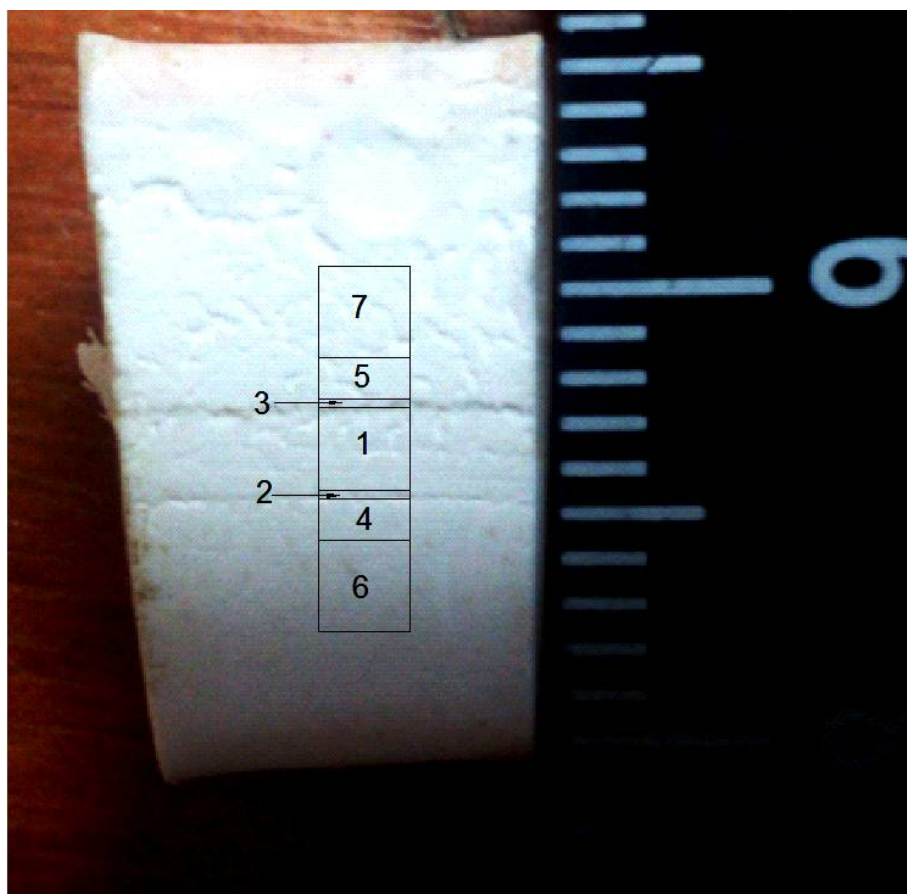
Зоны сварного раструбного соединения полипропиленовых труб
